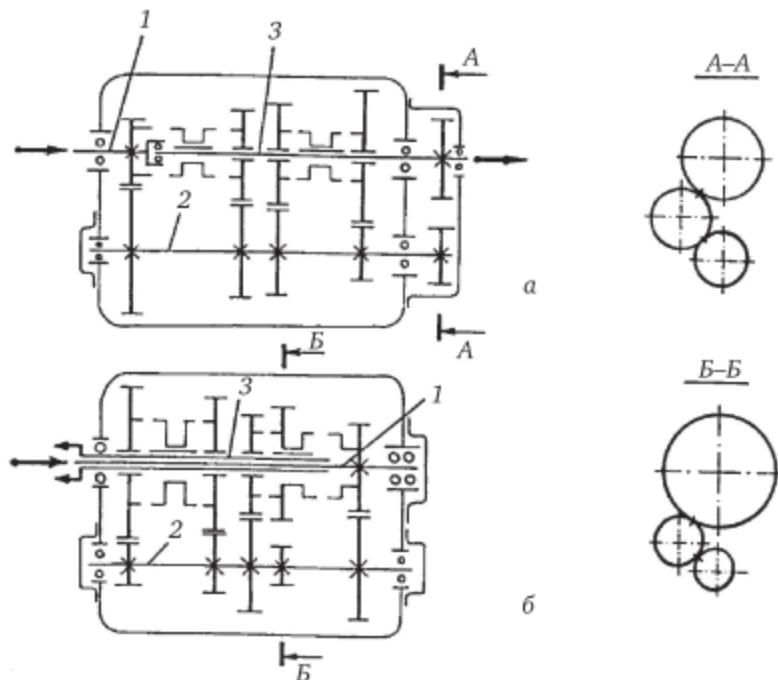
Кинематические схемы 3-вальниых коробок передач:
